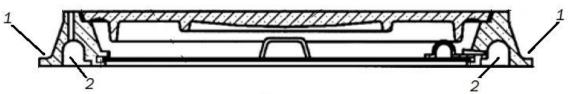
Детали корпуса чугунного люка лёгкого типа: 1 — фланец корпуса люка; 2 — кольцевая выемка в корпусе люка.
